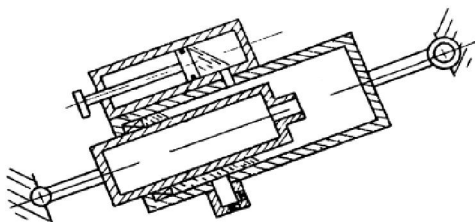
Пневматичний зрівноважувальний механізм з компенсатором
